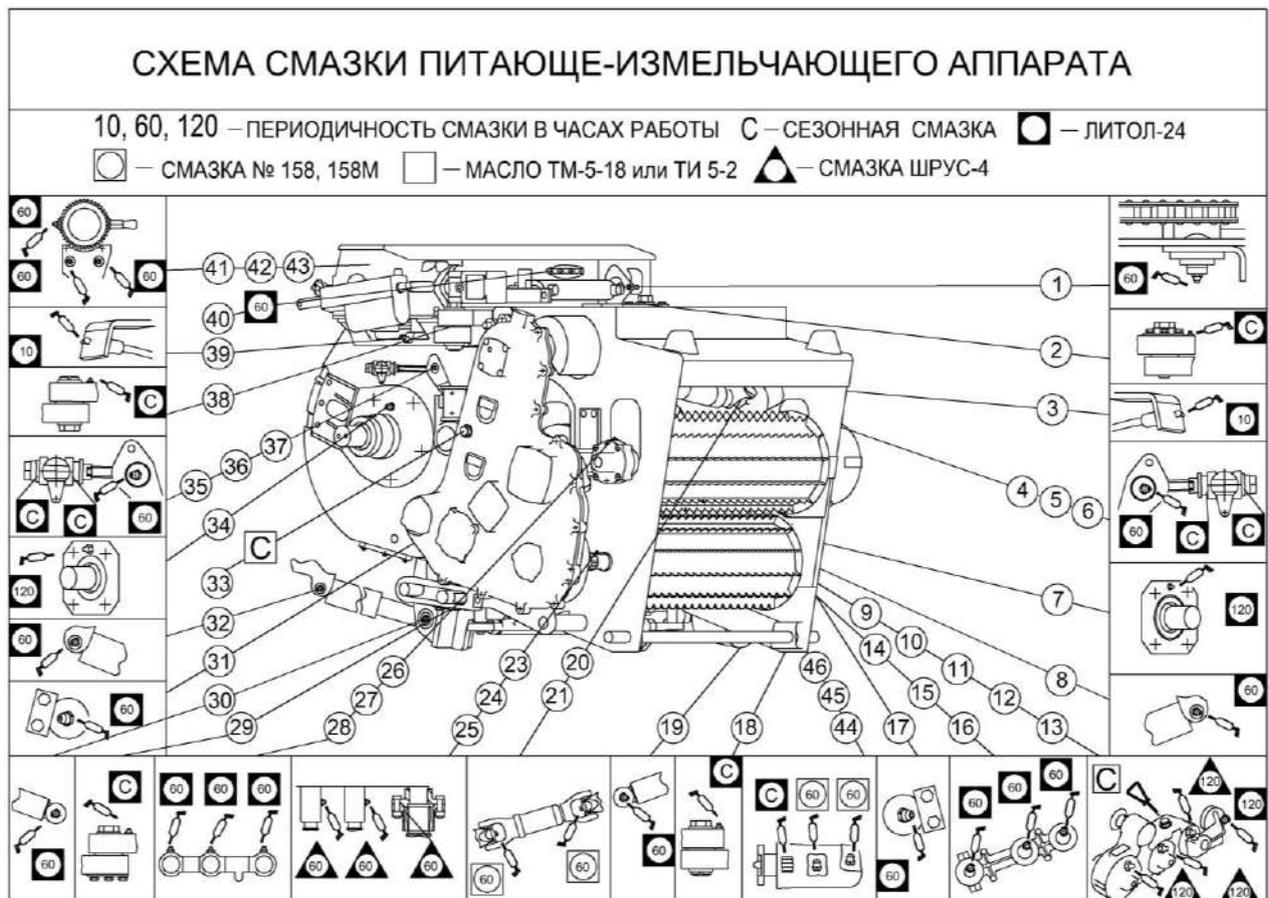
Схема смазки питающе-измельчающего аппарата комбайна
